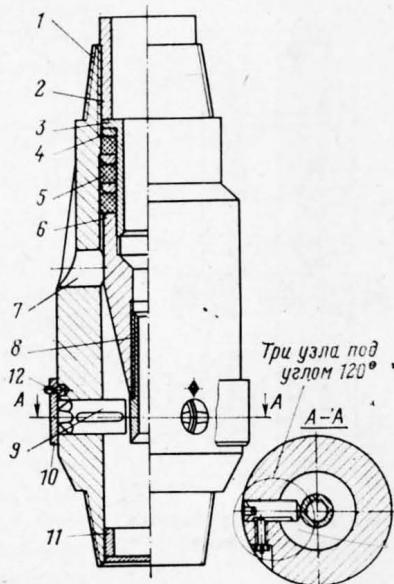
Труборезка-труболовка с силовым корпусом:
